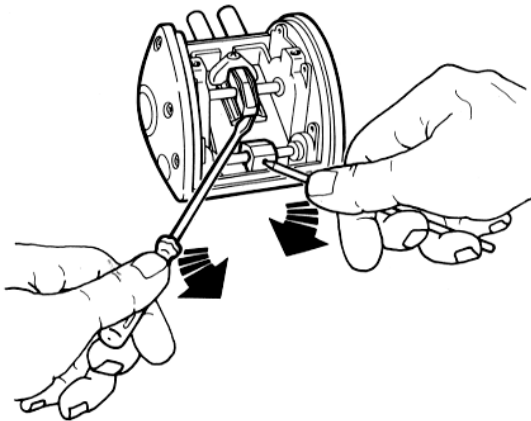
Smontaggio cassetto e valvola di inversione (fase 2)
